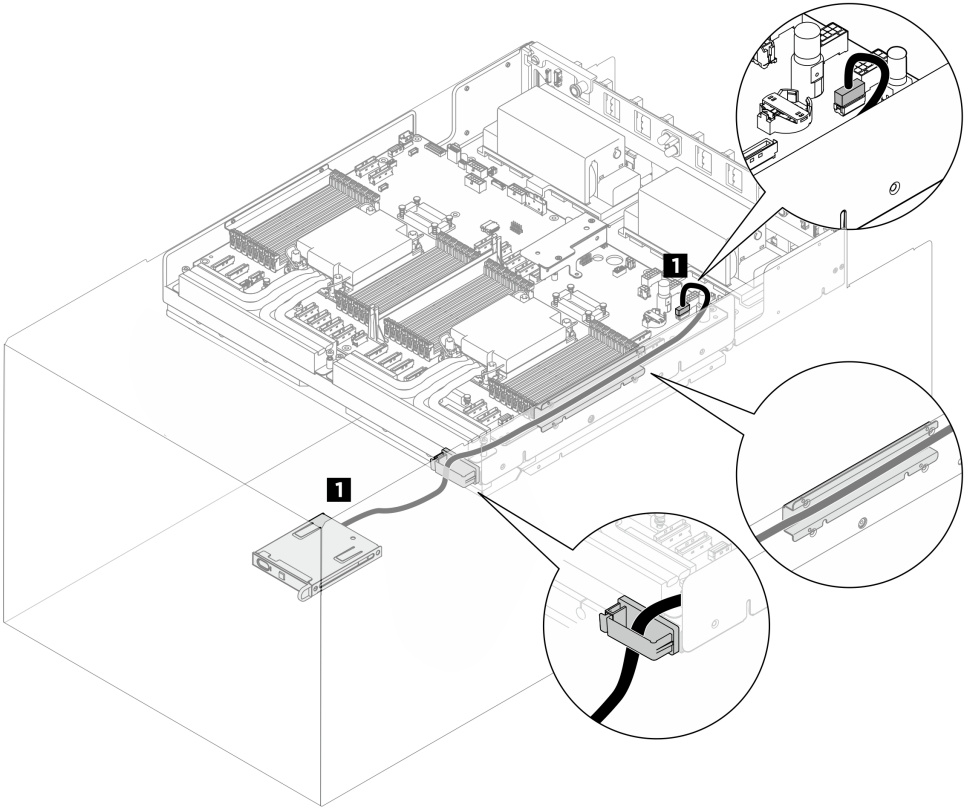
Disposición de los cables del panel de diagnóstico integrado
